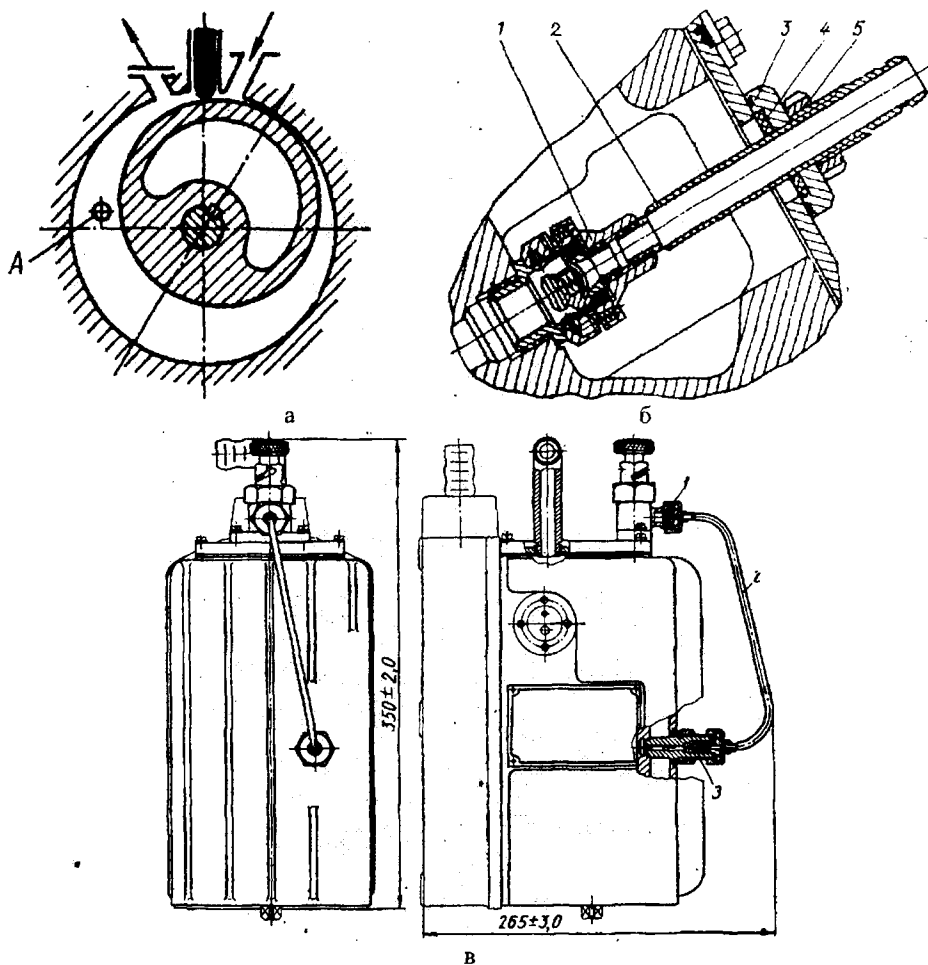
Газобалластный вакуумный насос:
